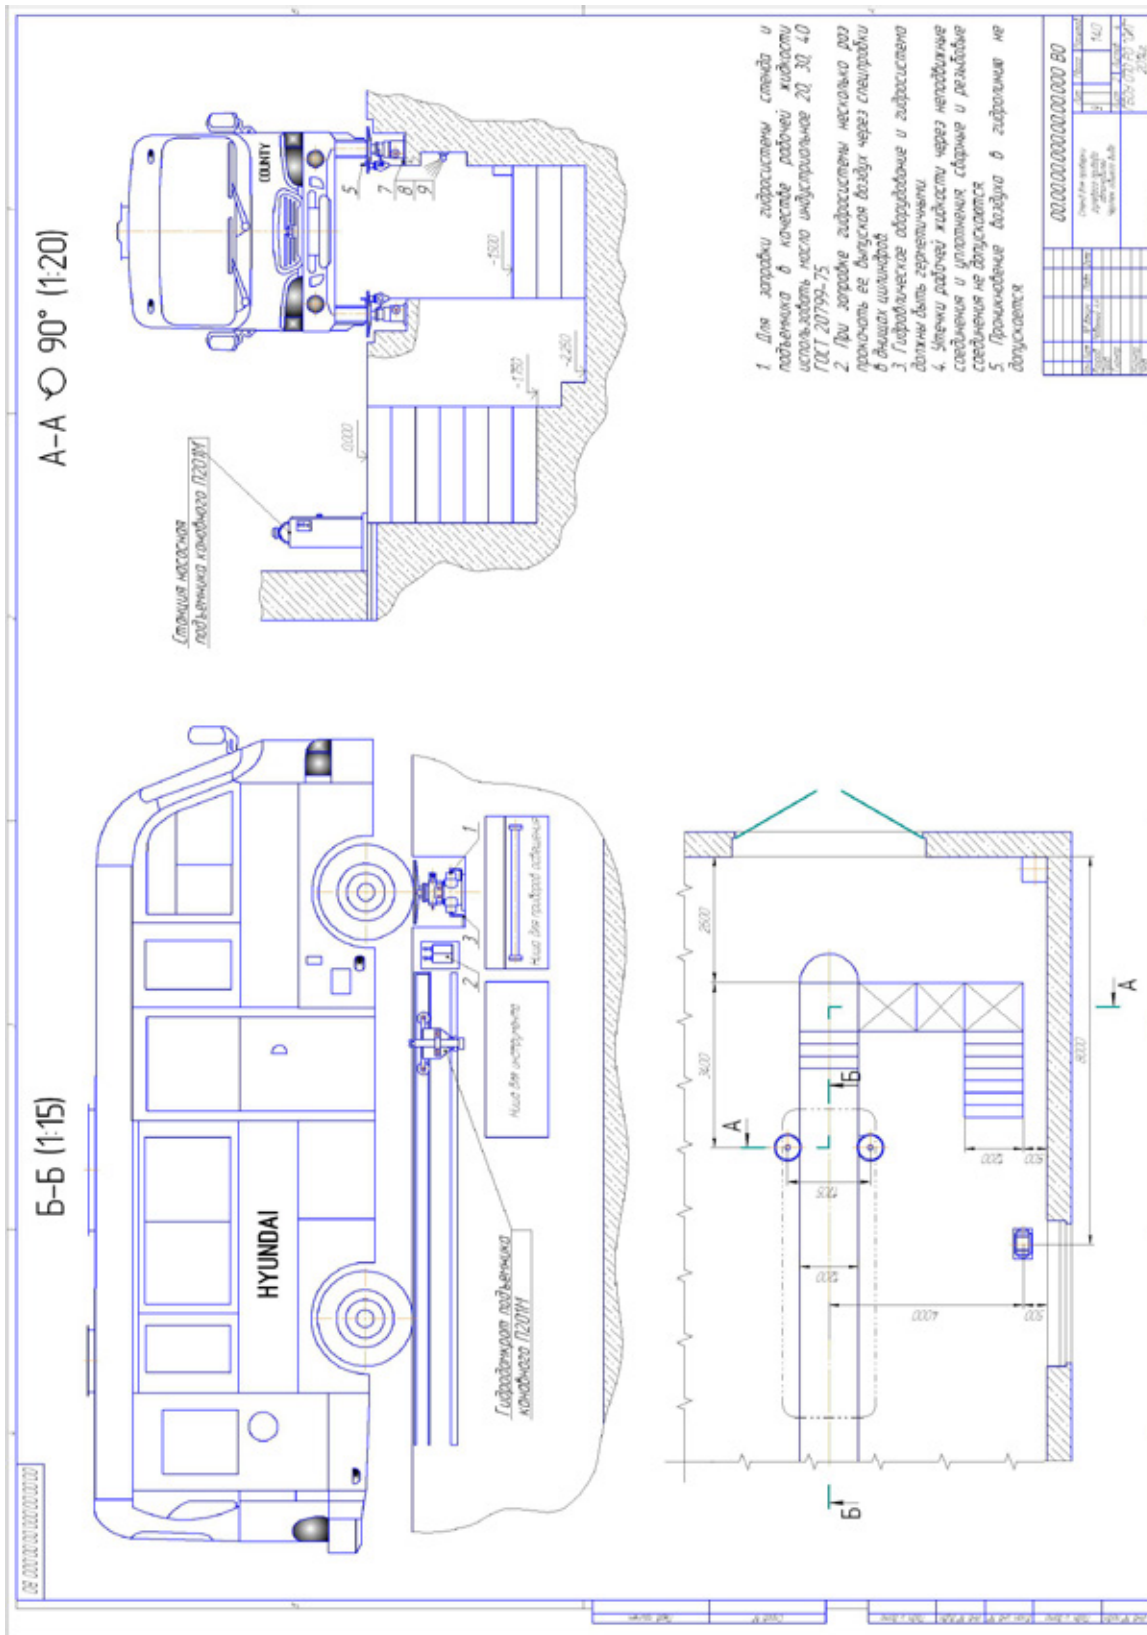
Чертеж общего вида стенда для проверки рулевого привода автомобилей
